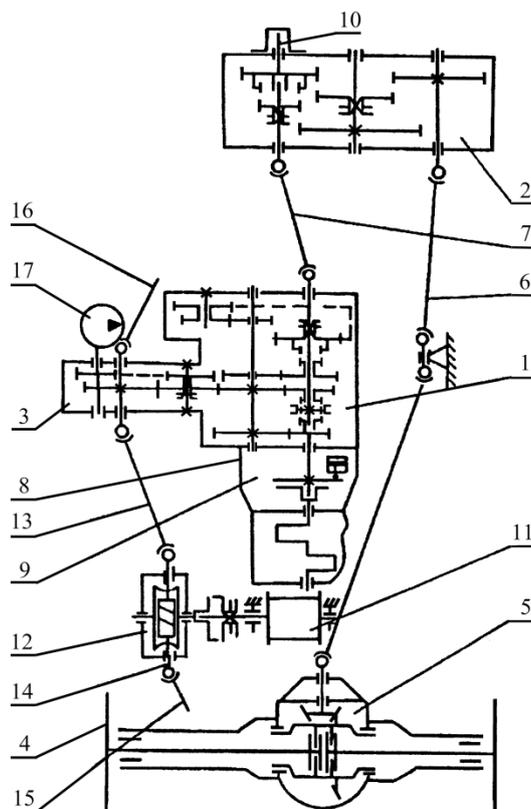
Кинематическая схема автотрактора: 1 – коробка перемены передач; 2 – раздаточная коробка; 3 – коробка отбора мощности; 4 – задний мост; 5 – самоблокирующийся дифференциал; 6, 7, 13 – карданные передачи; 8, 9 – корпус и муфта сцепления; 10 – передний ВОМ; 11 – тяговая лебедка; 12 – червячный редуктор; 14 – вал привода отбора мощности; 15 – задний ВОМ; 16 – средний ВОМ; 17 – гидронасос
